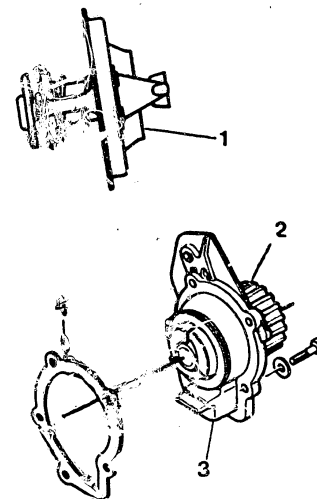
Oben: der Thermostat, 1 zeigt die äussere Seite, unten: 2 Pumpenantriebsrad - 3 Pumpengehäuse - 4 Dichtung.
